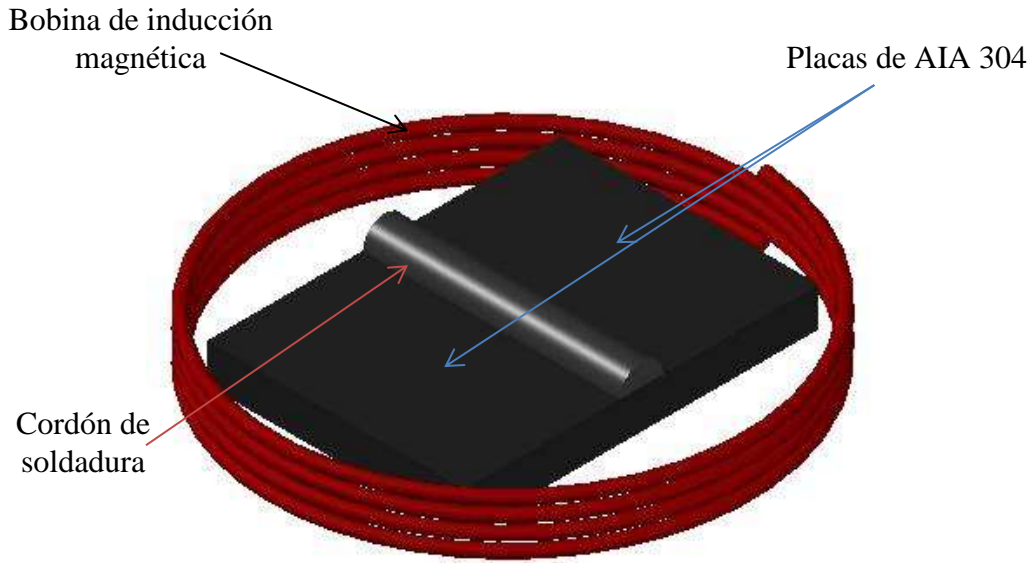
Esquema representativo de la configuración del campo magnético perpendicular a la dirección de aplicación del cordón de soldadura.
